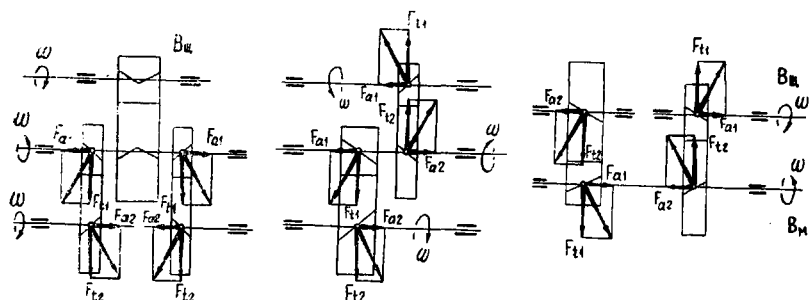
К выбору направления винтовых линий в цилиндрических колесах с косыми зубьями.
